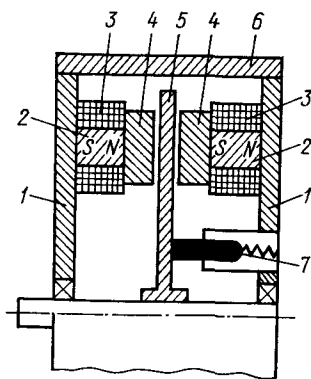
Конструктивная схема дискового двигателя с печатным якорем
